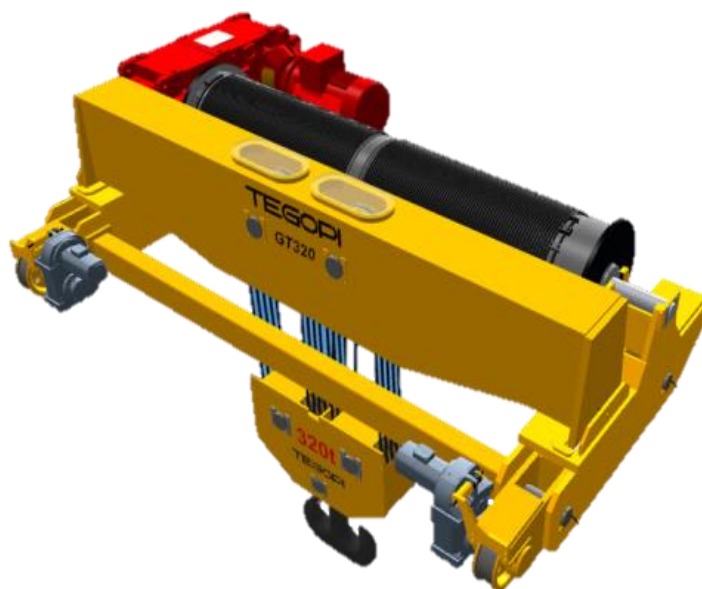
Sistema de Elevação de 320 Ton da TEGOPI SA em 3D
